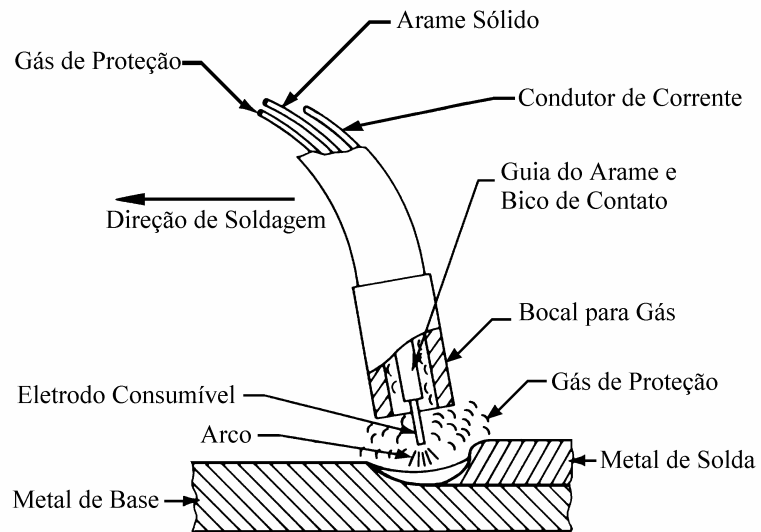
Processo de soldagem GMAW (AWS, 1991).
